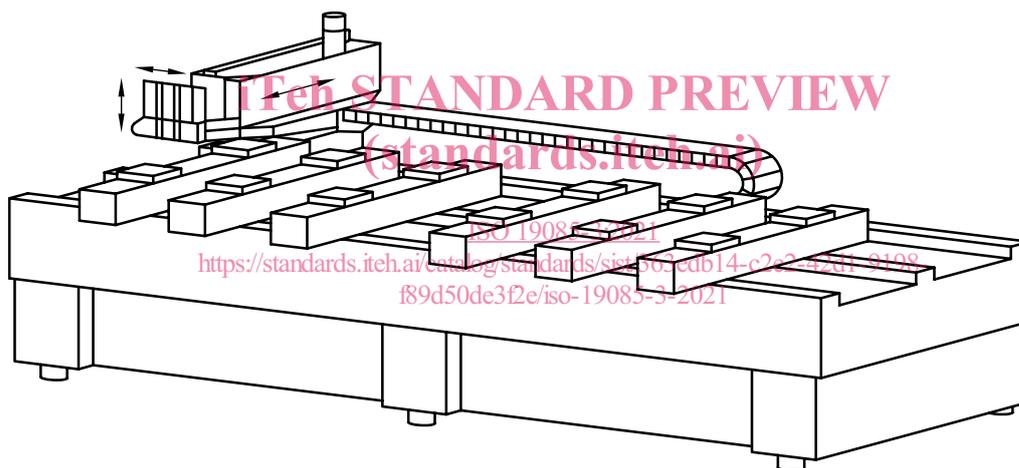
Exemple de machine à bâti en col de cygne avec table fixe et tête d'usinage mobile
